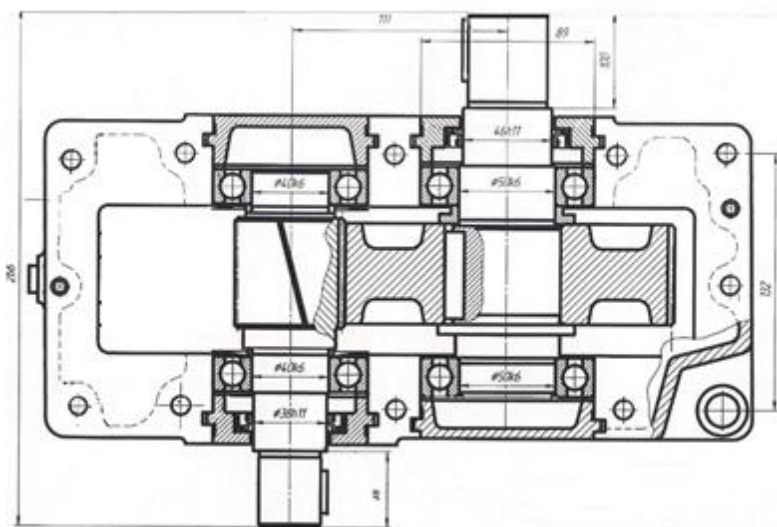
Чертеж цилиндрического одноступенчатого редуктора с шариковыми радиальными подшипниками
